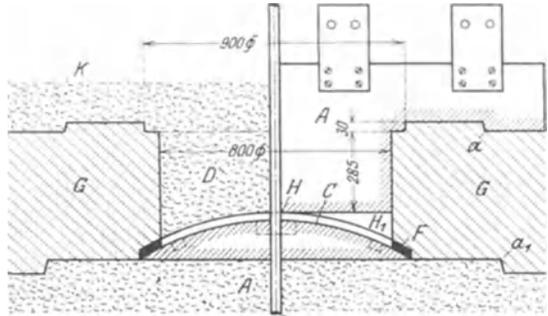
Mantel- und Oberkasten zu Fig. 117.
